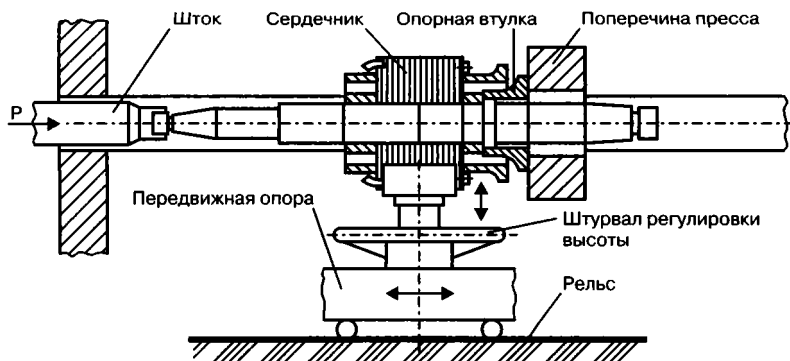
Схема выпрессовки вала из сердечников ротора
